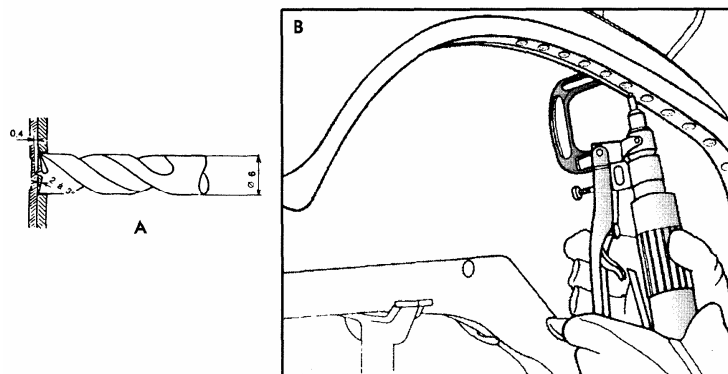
Corte en punto de soldadura con taladro de mano.
